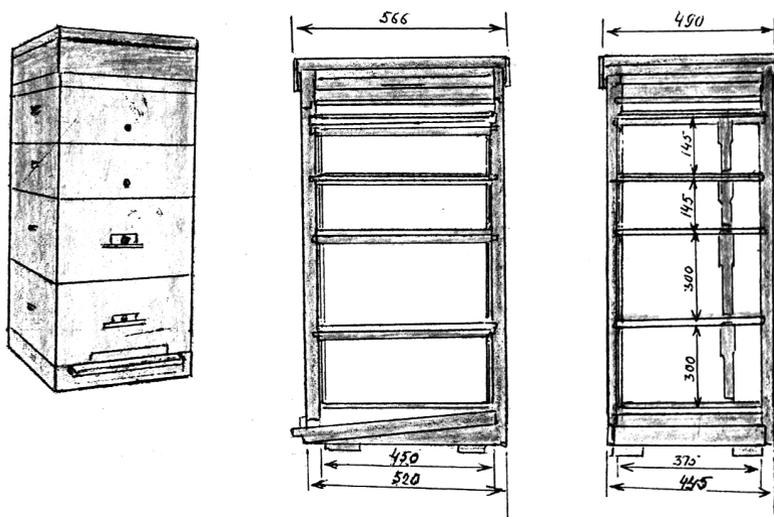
Двухкорпусный улей с надставками, типовой проект 3.808-2
